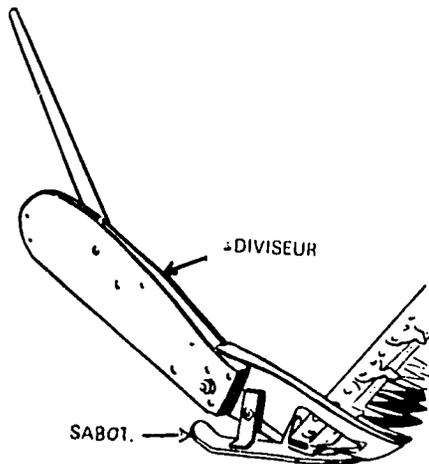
Diviseur et sabot sont des pièces importantes de la faucheuse
